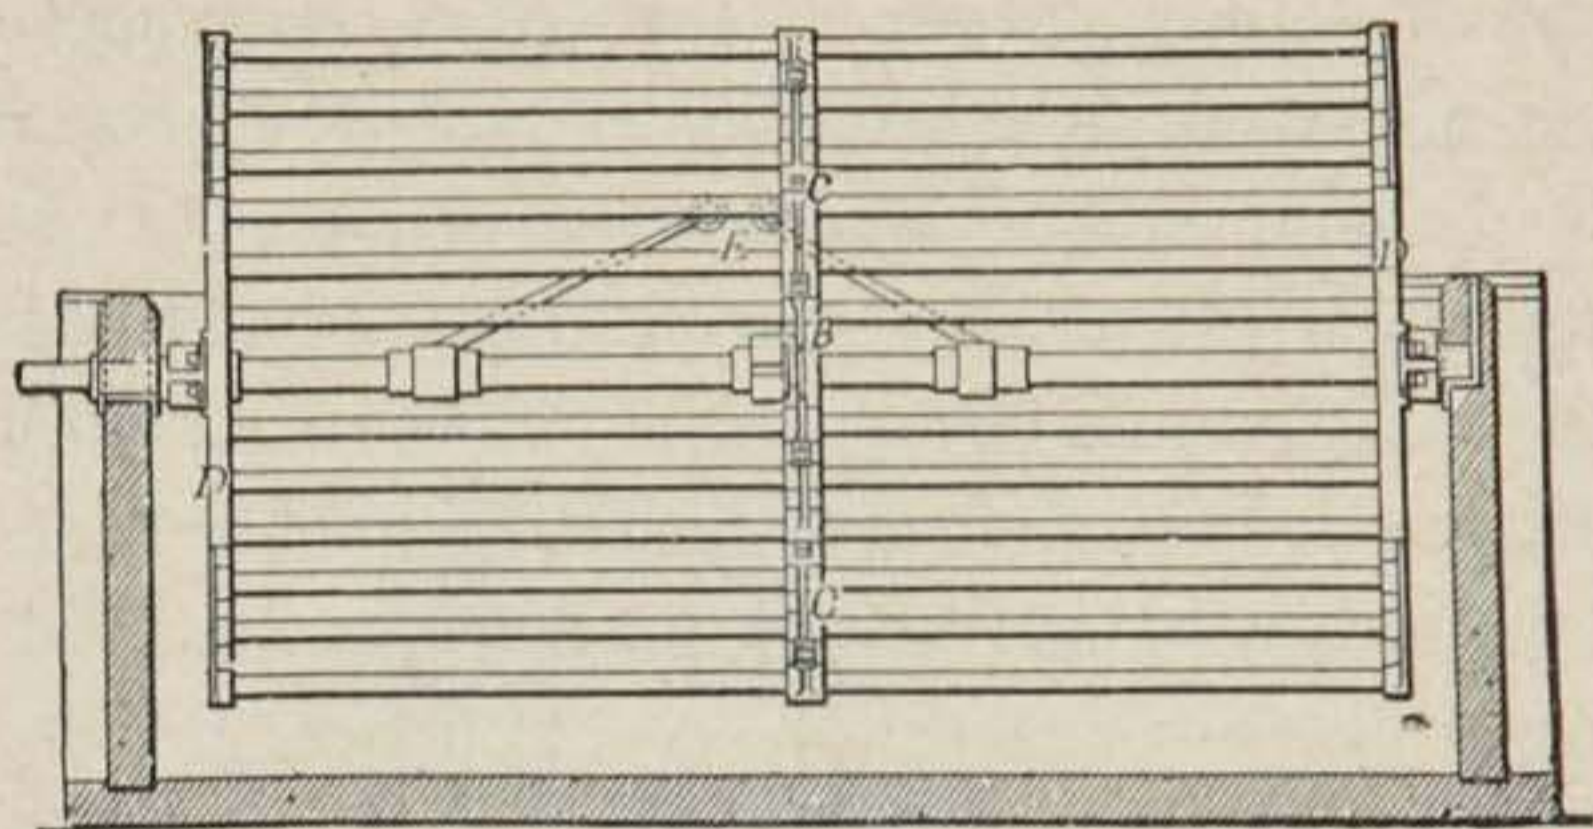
Machine à teindre de Wilson et Paisley. (face)
